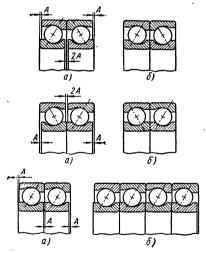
Установка сдвоенных радиальноупорных подшипников: a — до монтажа; δ — после затяжки на валу и в корпусе
